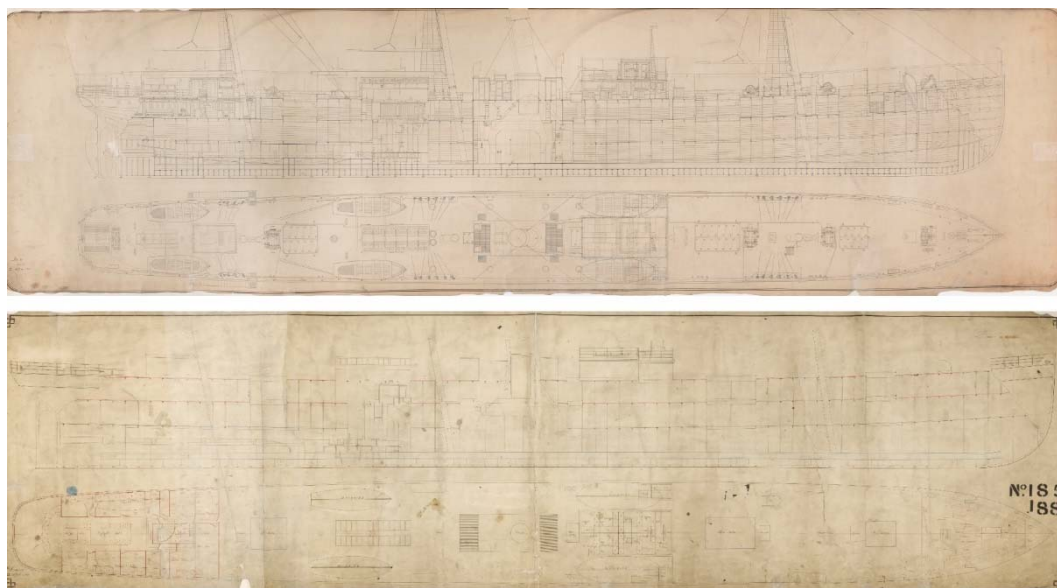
Planos de construção do *Childwall Hall*. Fonte: *Science Museum Group*, Londres.
